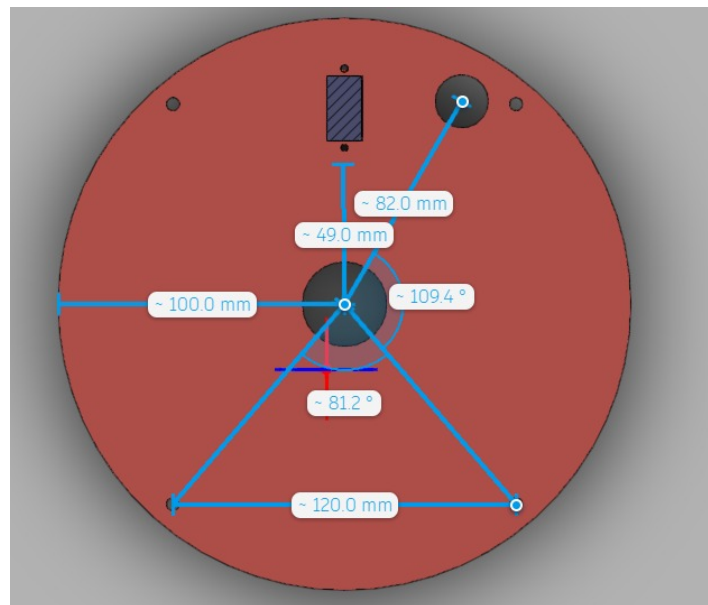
Plano y dimensiones de la base principal del robot manipulador o el nivel superior del robot diferencial
